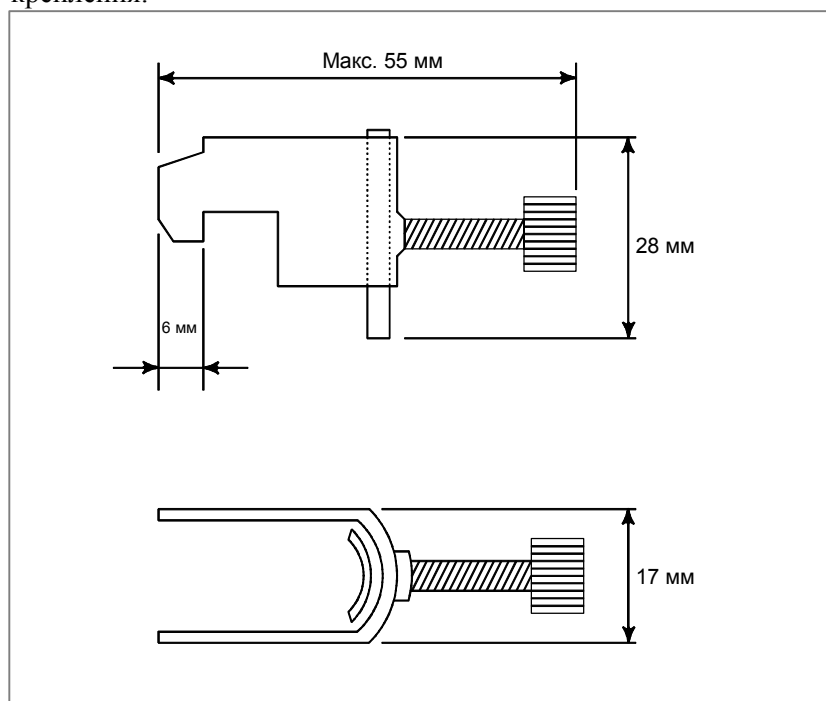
(e) Габаритные чертежи металлической арматуры для крепления
